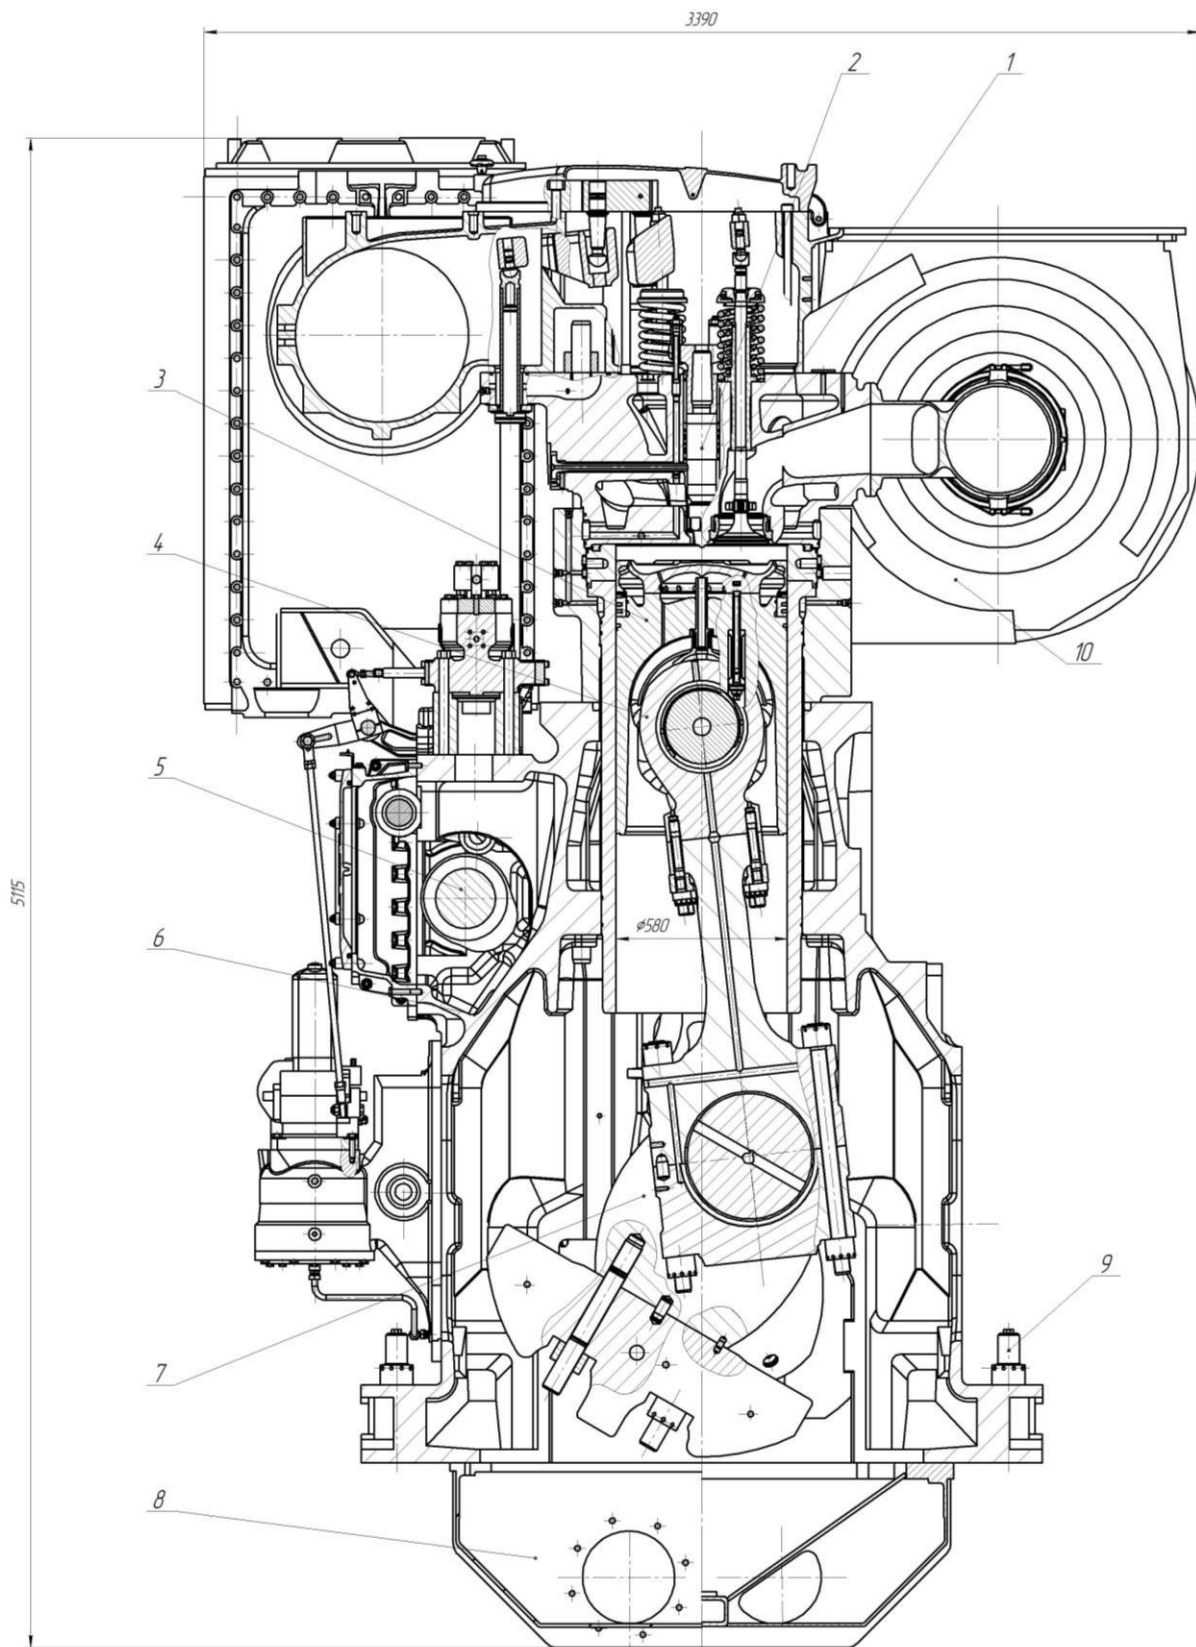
Поперечний переріз дизеля 8L 58/64: 1 – випускний клапан; 2 – форсунка; 3 - поршень; 4 – шатун; 5 – розподільний вал; 6- станина; 7 – колінчастий вал; 8 – фундаментна рама; 9 – анкерний болт; 10 – газова турбіна
